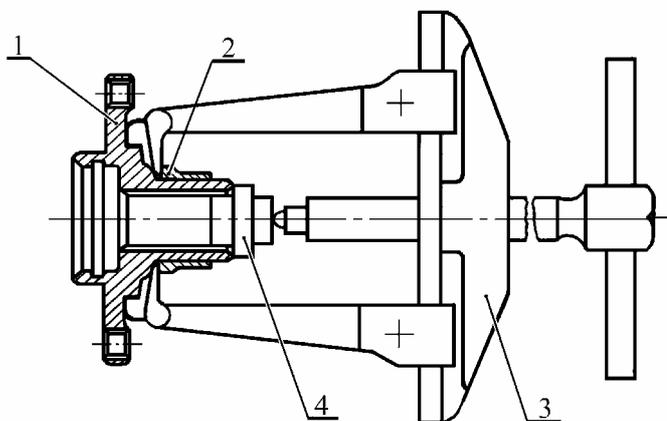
Спрессовка внутреннего кольца подшипника со ступицы переднего колеса:
